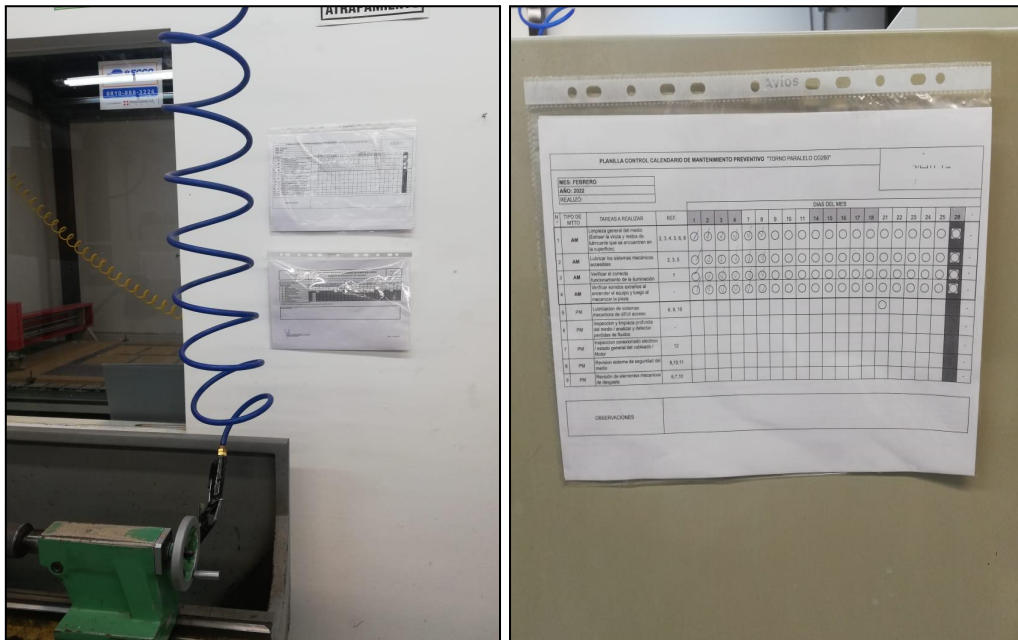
Calendario de mantenimiento en las máquinas (Torno Paralelo CQ260 y Torno CNC Lathe Machine CK6136A) [Fuente: Institucional]
